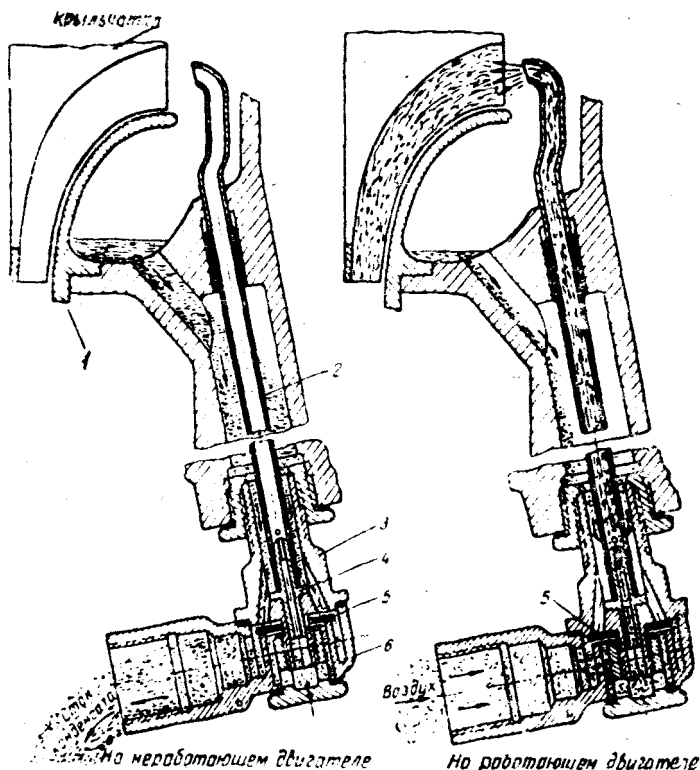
Схема устройства и работы комбинированного клапана нагнетателя: 1—диффузор; 2—трубка клапана; 3—корпус; 4—распылитель; 5—подвижная шайба; 6—ниппель
